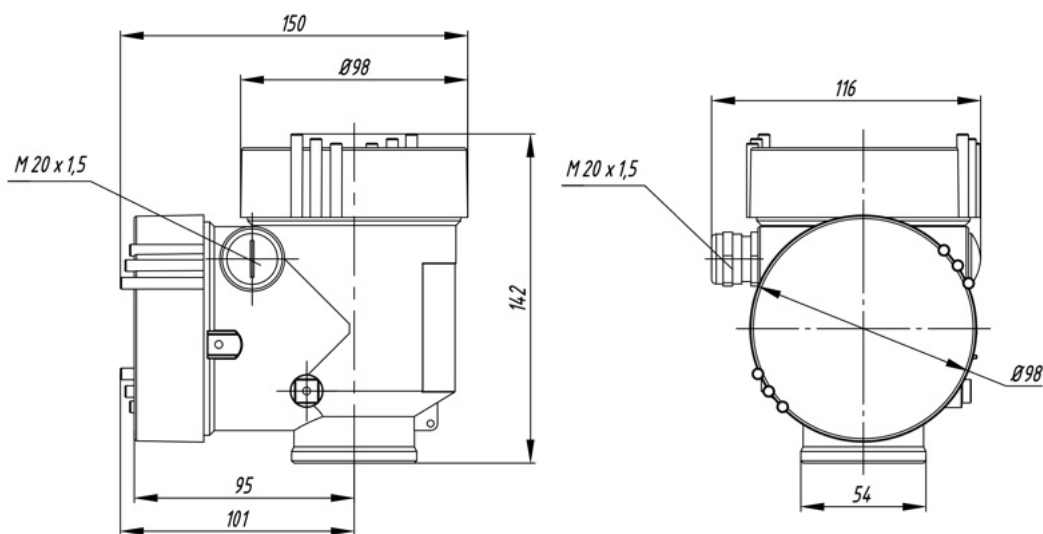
Корпус из алюминиевого сплава с 2 отсеками
